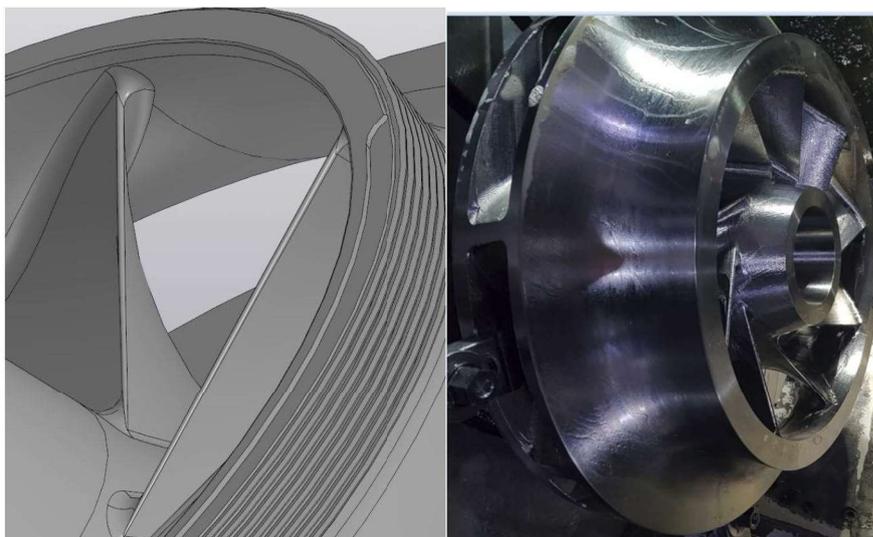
Твердотельная модель и внешний вид рабочего колеса компрессора ТК26, диаметр 475 мм, мощность 8000 кВт
